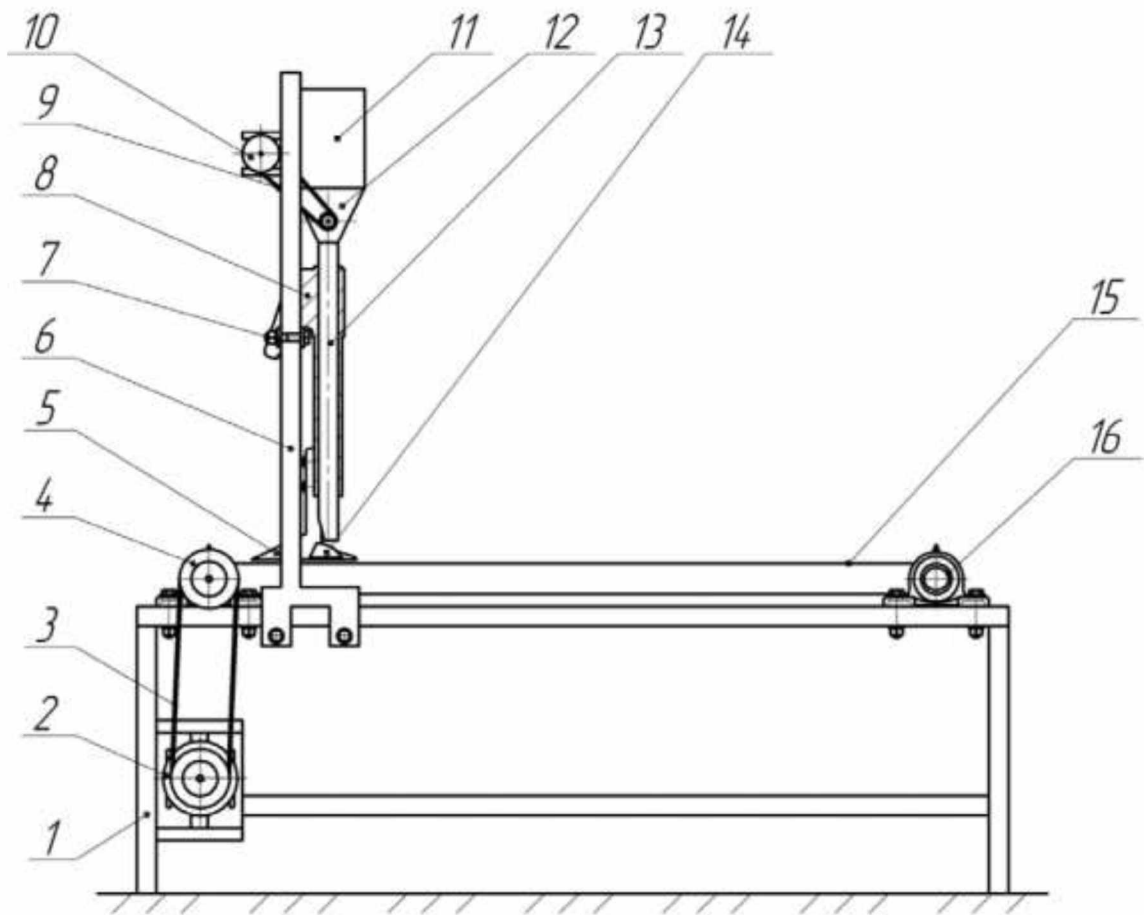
Схема лабораторної установки: 1 - рама; 2 - електродвигун стрічки транспортера; 3 - ремінна передача стрічки транспортера; 4 - ведучий вал; 5 - сошник; 6 - опора для кріплення висіваючої системи; 7 - перекладина; 8 - стійка сошника; 9 - ремінна передача посівного апарату; 10 - електродвигун висівного апарату; 11 - ящик для насіння; 12 - висіваючий апарат; 13 - насіннепровід; 14 - розподільник; 15 - стрічка транспортера; 16 - ведений вал
